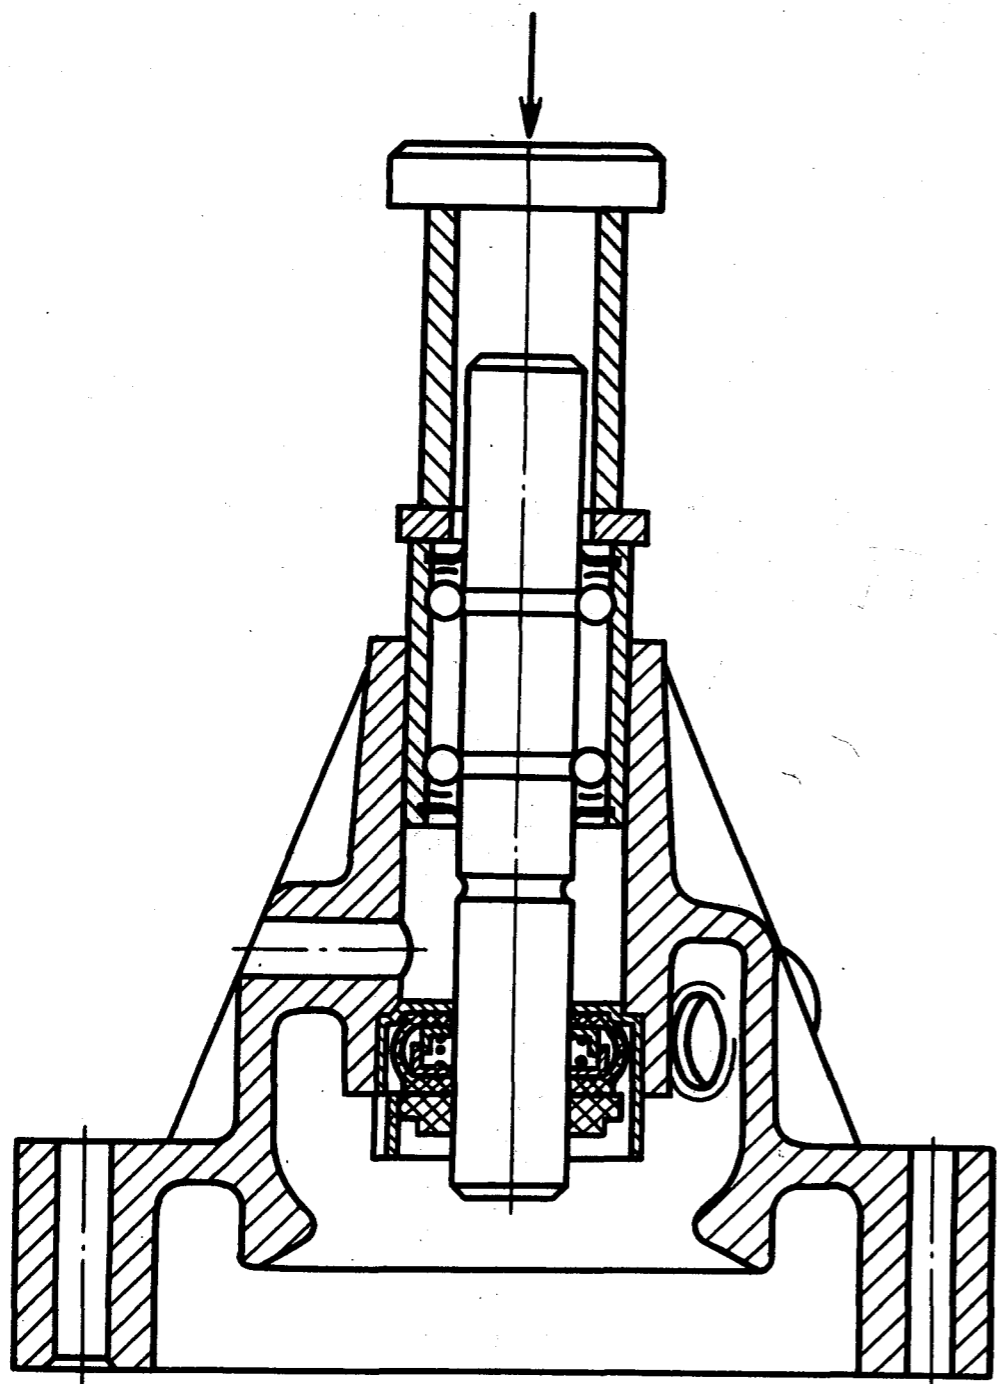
Запрессовка подшипника с валком водяного насоса в корпусе
